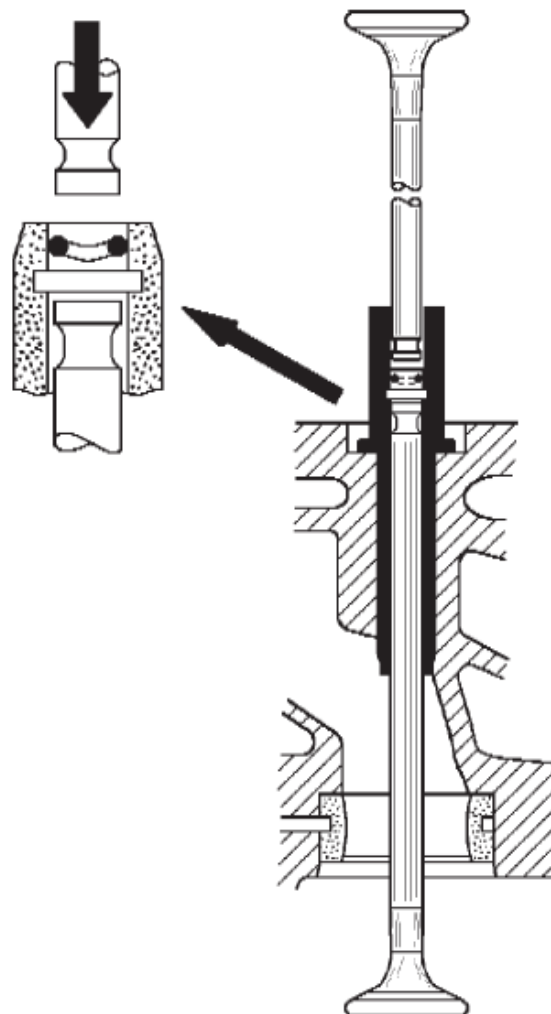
Установка нового О-кольца в направляющую клапана
